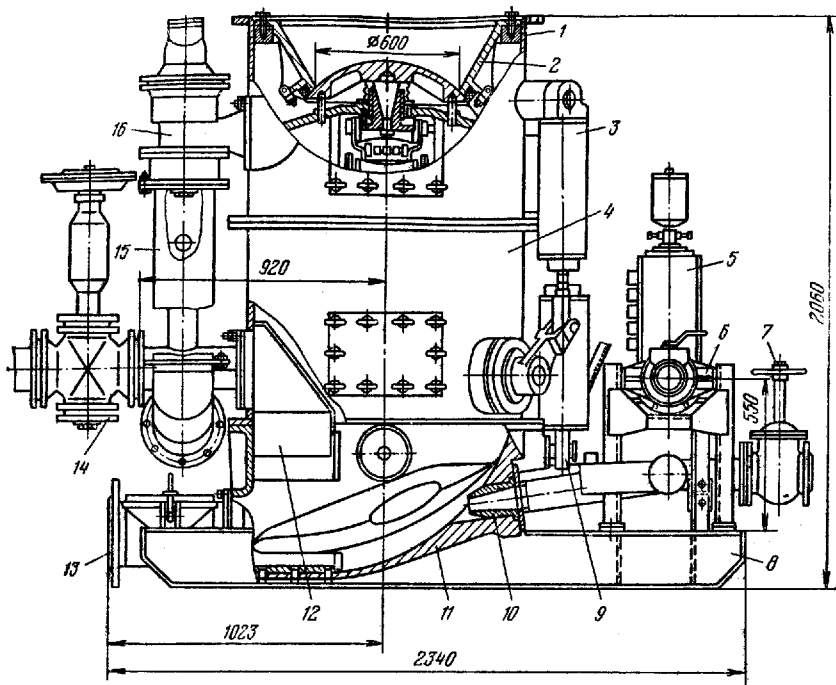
Пневмозакладочная машина двухкамерного типа ДЗМ2
